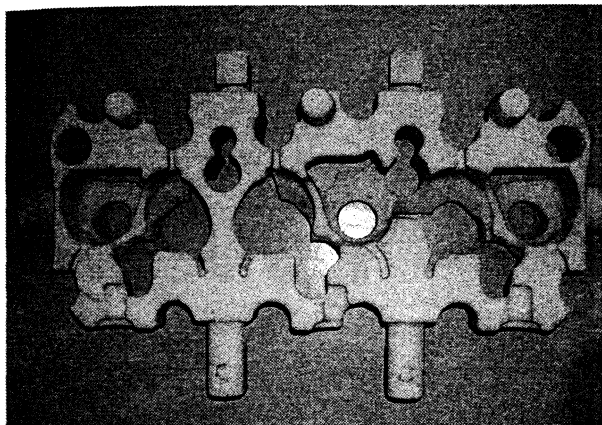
Сплошной стержень рубашки водяного охлаждения отливки «Головка блока цилиндров» № 260–1003015
